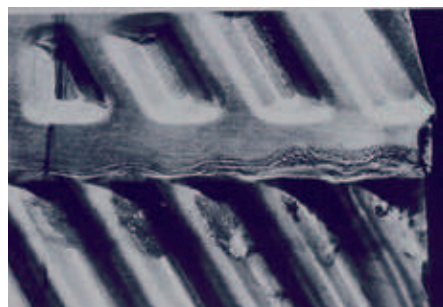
corrosion cavernueuse sur échangeur à plaque
